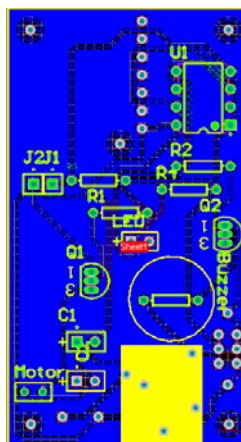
Diseño electrónico de la PCB (Capa inferior).
